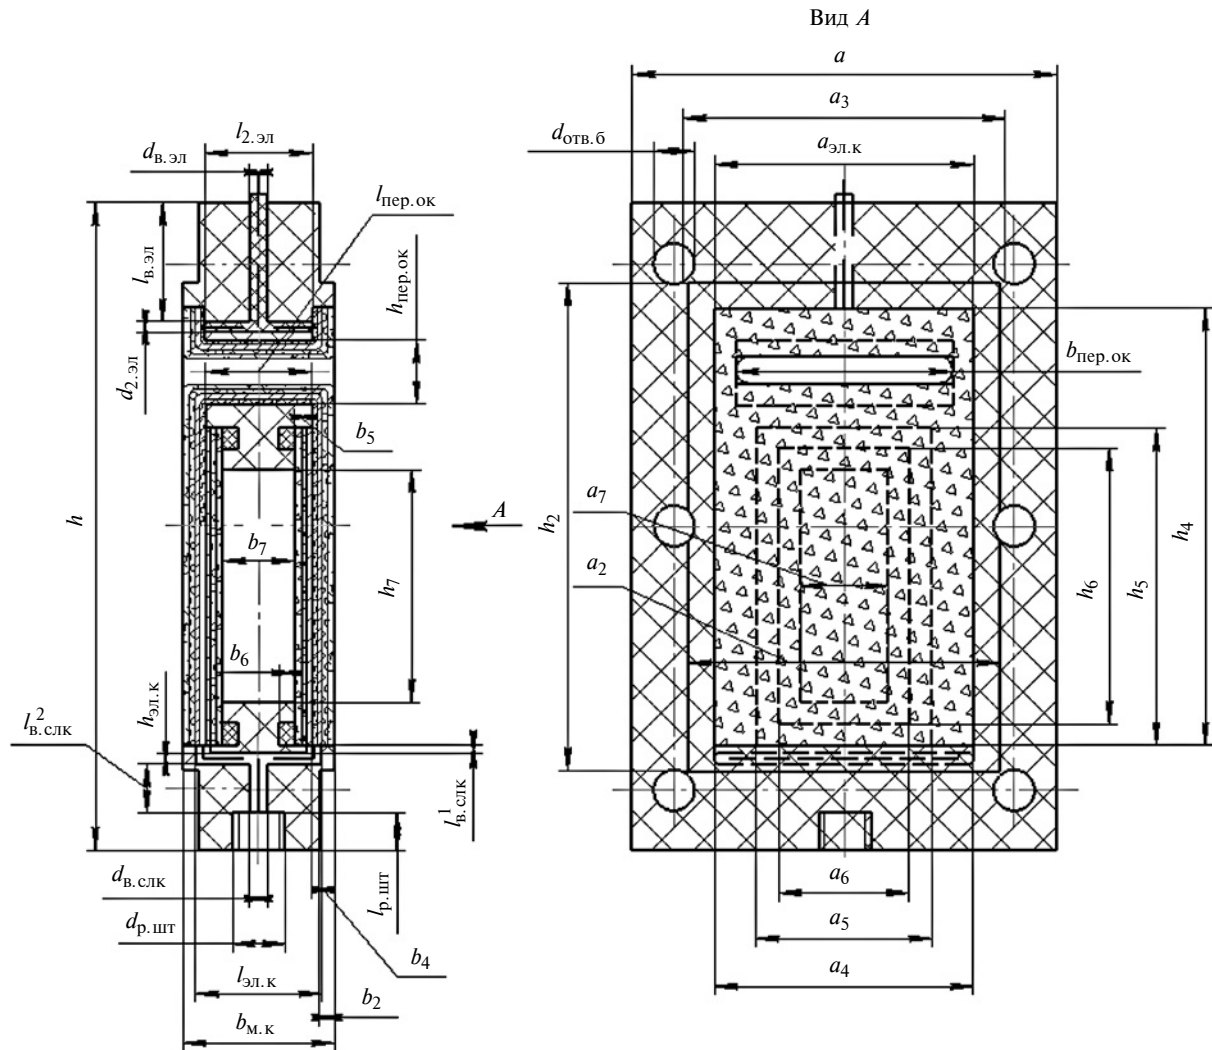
Расчетная схема объема малой камеры корпуса ЭБМПА
